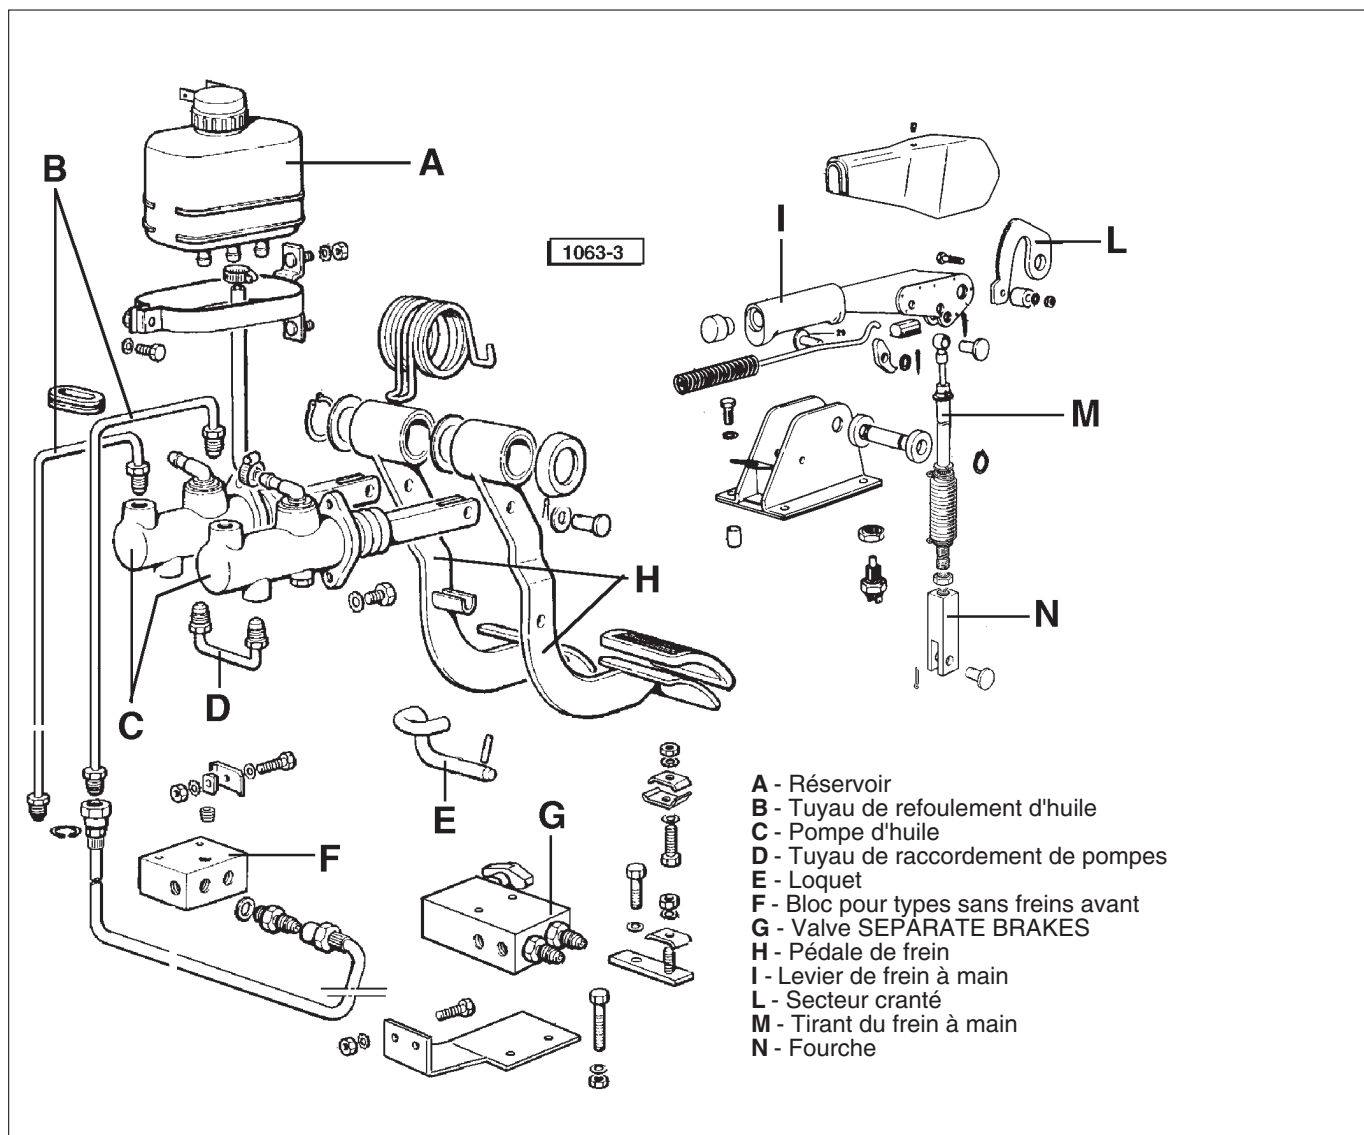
Pièces composant l'ensemble de commande des freins.
